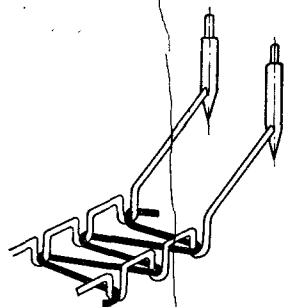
Трехниточный цепной стежок наружного переплетения
